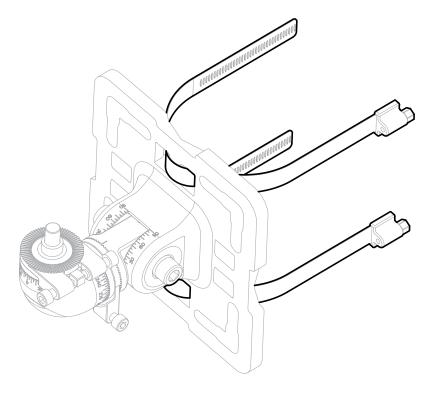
Montaggio della staffa di montaggio universale mediante fermagli per viti senza fine
